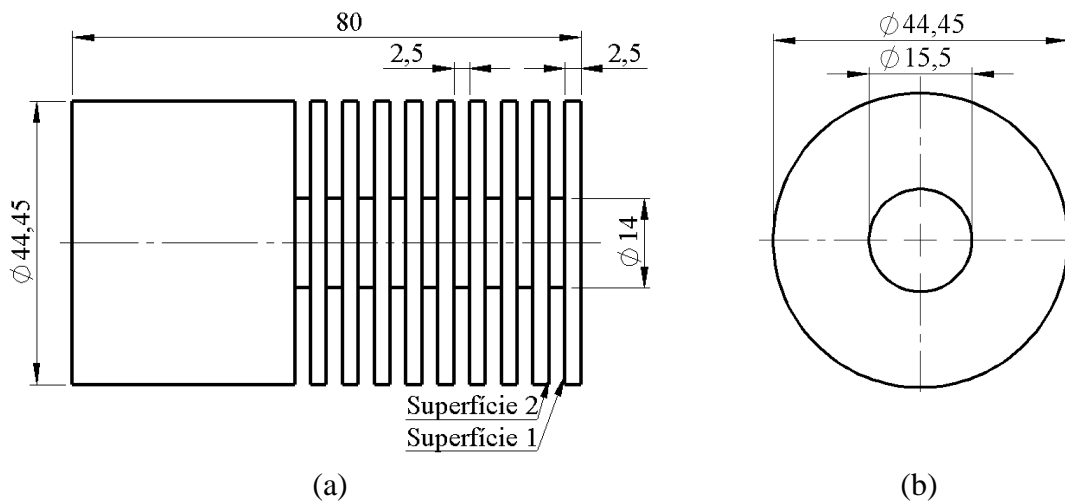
Corpo de prova referente à Etapa 3: (a) cortes; (b) anel (dimensões em mm).
